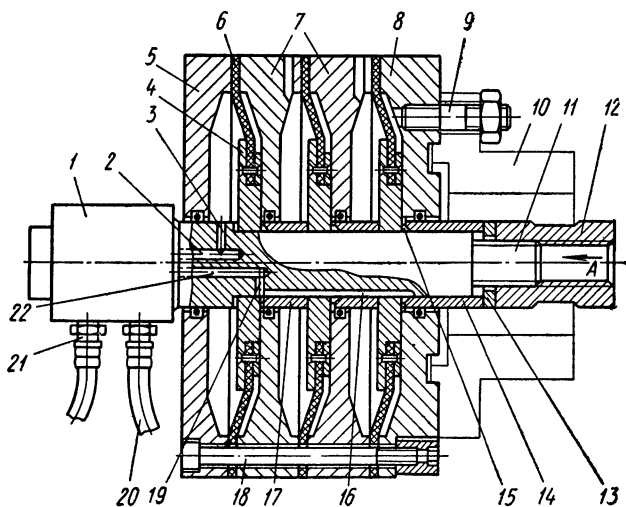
Вращающийся привод с несколькими пневмокаме-рами
